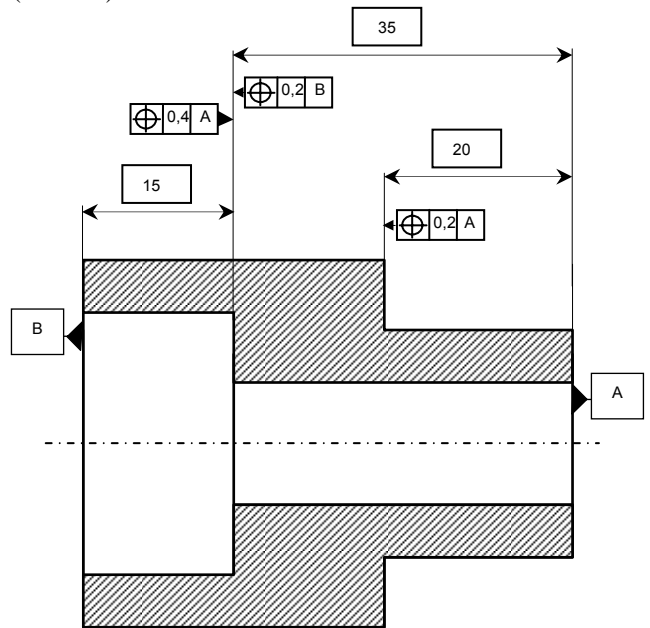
Dessin de définition de la pièce de tournage (une vue)
